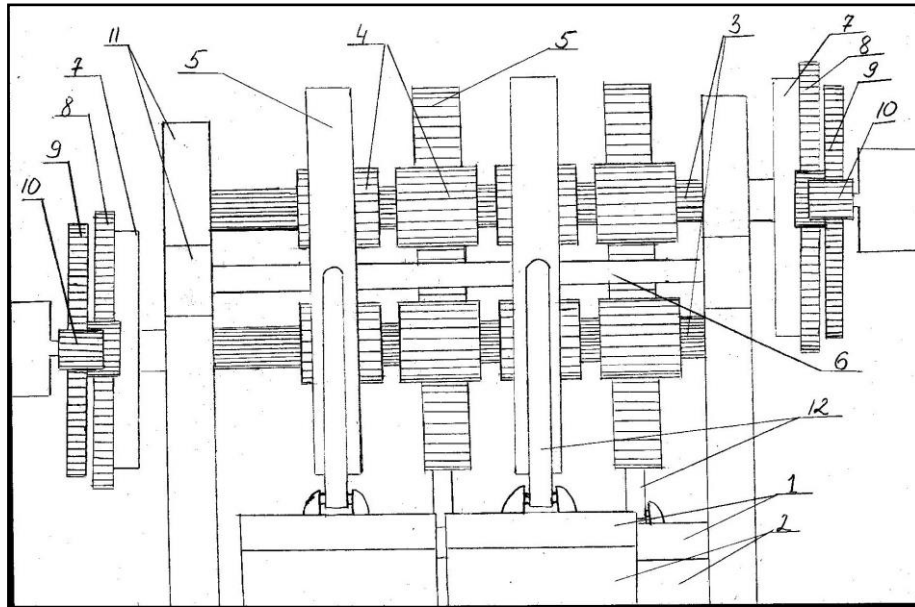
Волновой преобразователь шестеренчатая передача вид сбоку.
